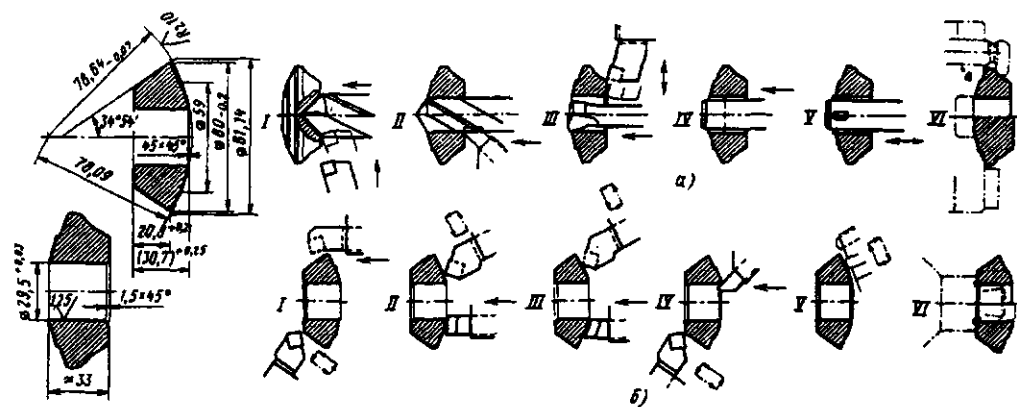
Наладки шестишпиндельных полуавтоматов для обработки штучных заготовок промежуточных зубчатых колес: а – базирование по наружной поверхности; б – базирование по обработанному внутреннему отверстию и торцу
